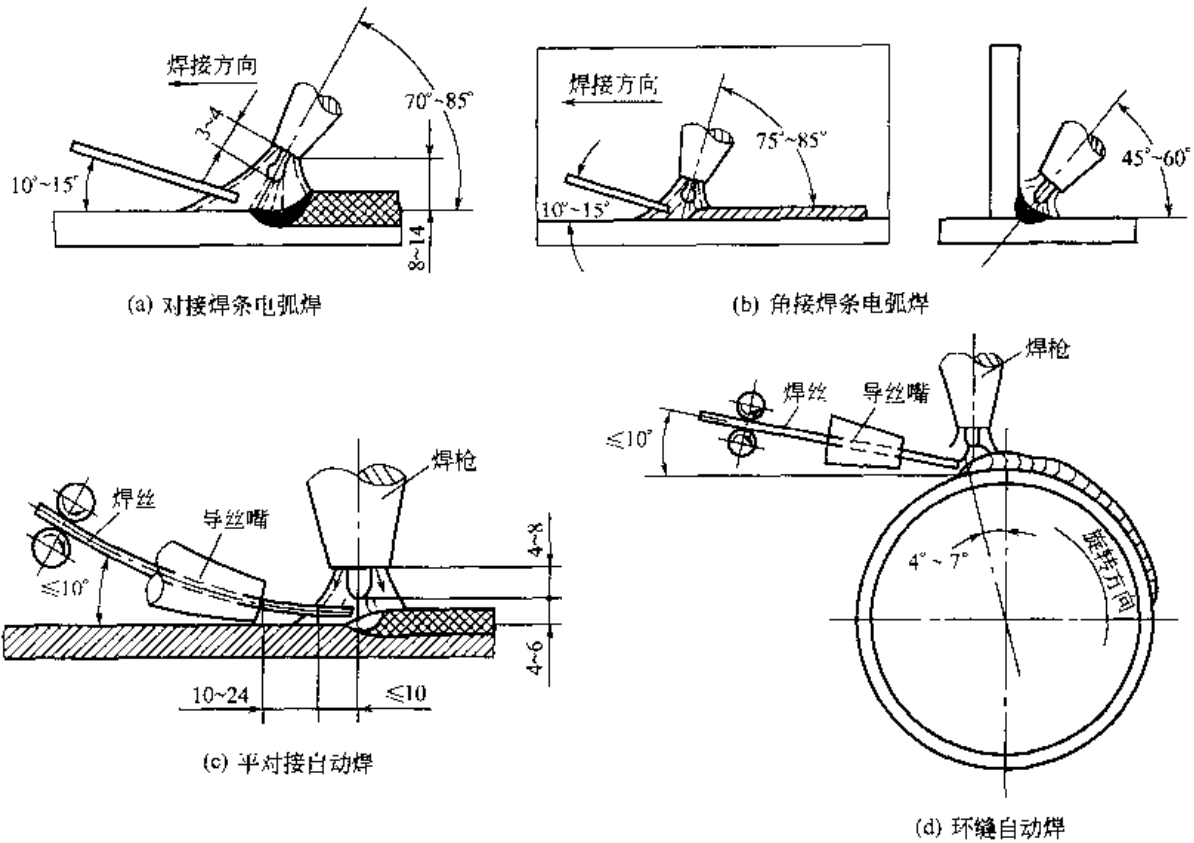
焊枪、焊丝和工件之间的相对位置
